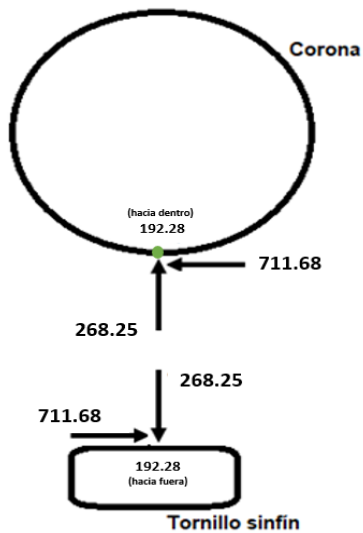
24. Fuerzas de transmisión en corona y tornillo sinfín.
